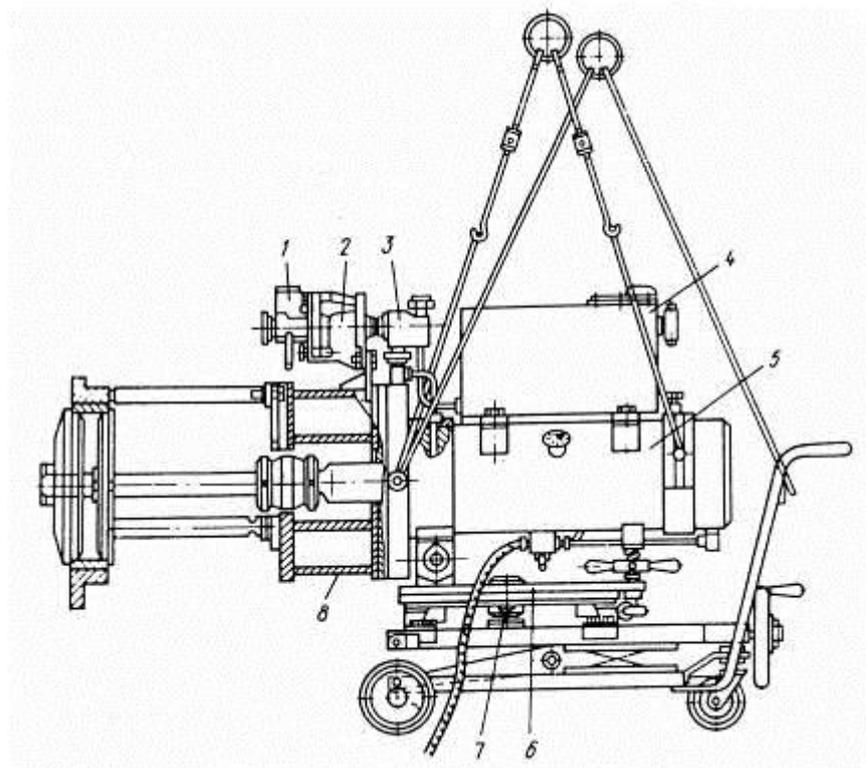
Передвижной пресс: 1 — пневматическая головка; 2 — воздушный цилиндр; 3 — клапанная коробка; 4 — бак для масла; 5 — цилиндр; 6 — поворотный стол; 7 — тележка; 8 — опорный барабан
